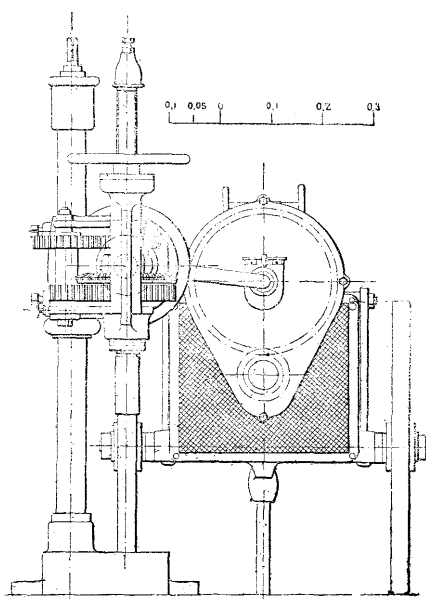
Perceuse mobile de MM. Collet et Engelhard, d'Offenbach. — Vue par bout.
